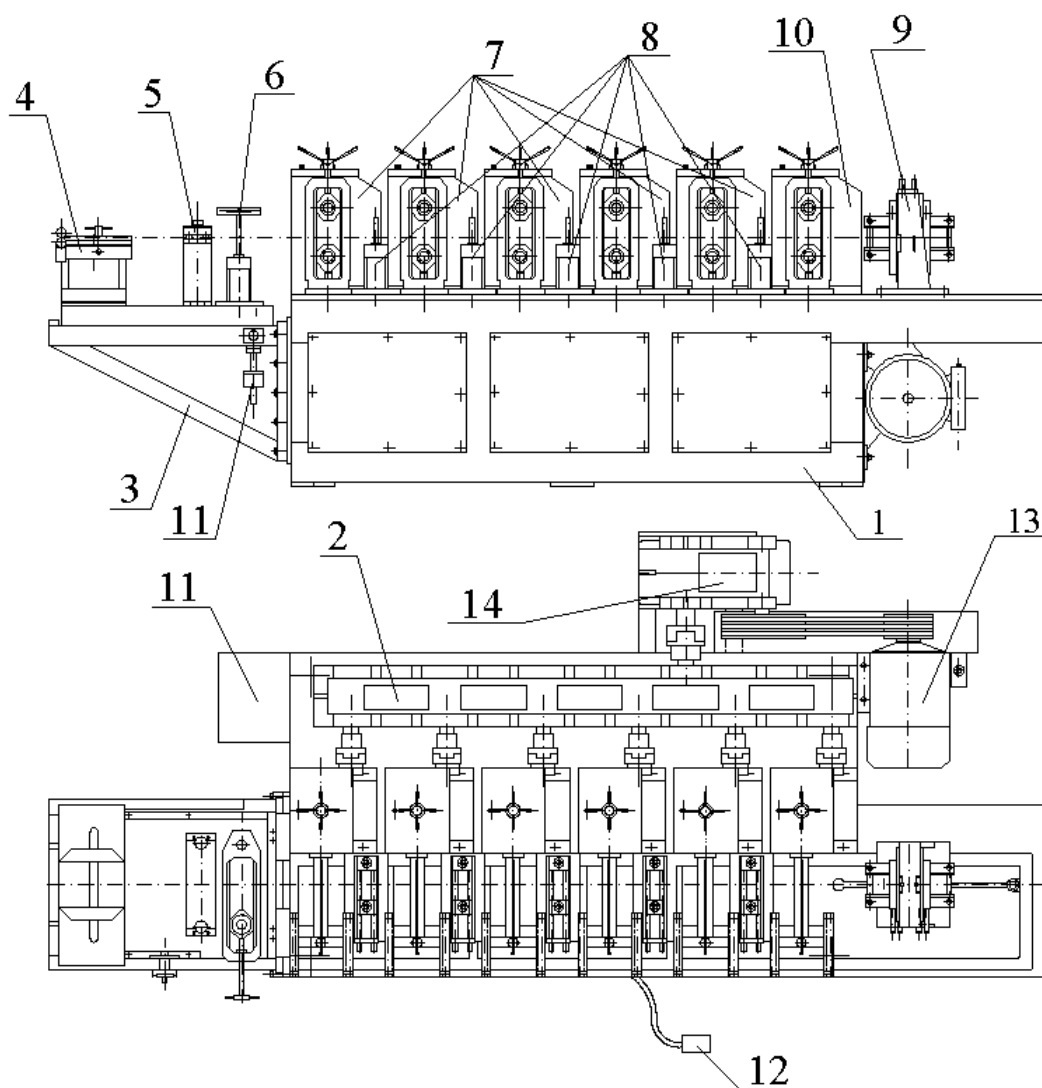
Схема гибочно-прокатного станка ГПС-350М6
